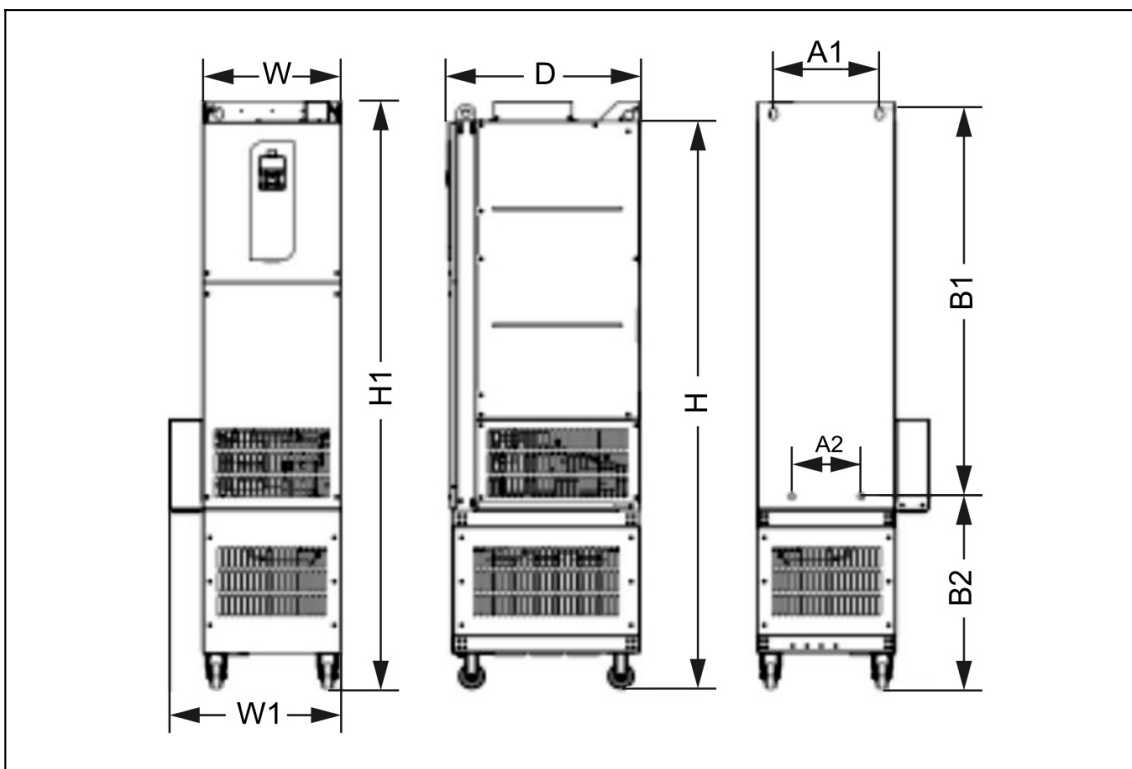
Размеры корпусов Т8-Т10 с дополнительным основанием
